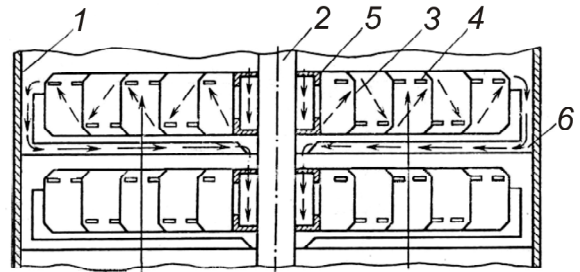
Відцентровий апарат конструкції ДІАП: 1 – корпус; 2 – вал; 3 – коаксійні циліндри; 4 – перфорація; 5 – розподільчий пристрій; 6 – переливна тарілка
